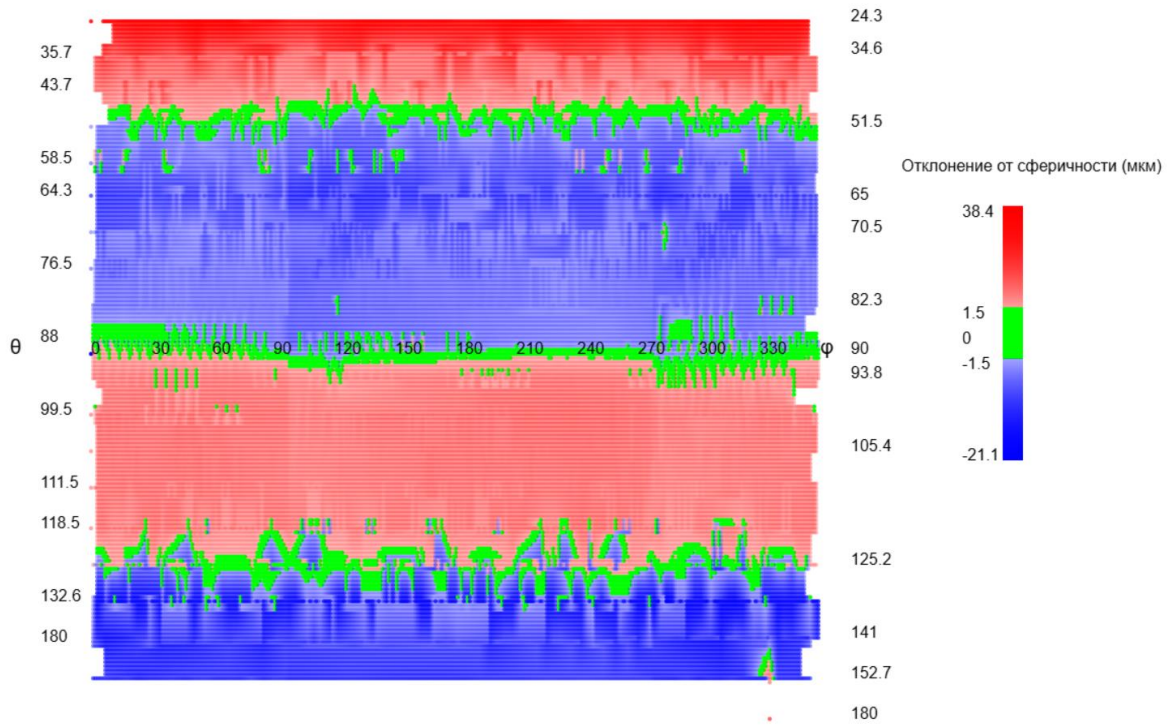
Развертка сферической поверхности шарового пальца №3 до притирки
